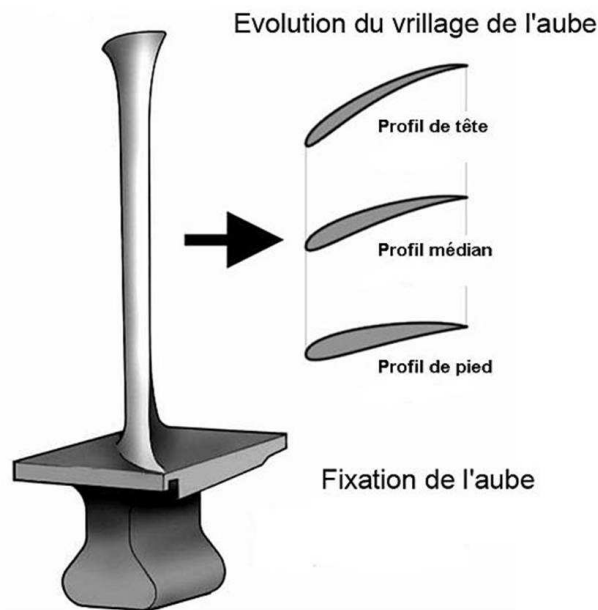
Forme et profil d'une aube de turbine.
